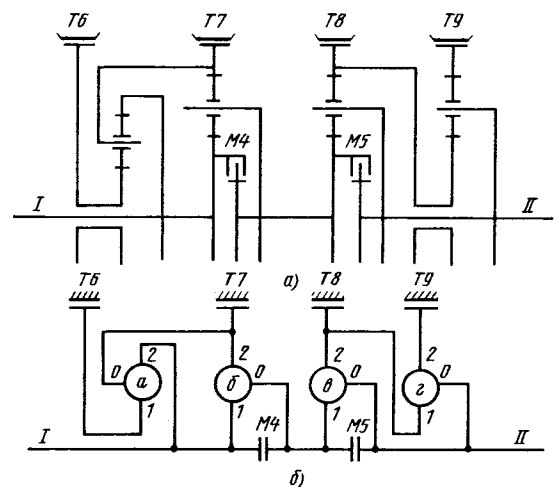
Кинематическая схема планетарной коробки передач (а) и схема силового потока планетарной коробки передач (б)
